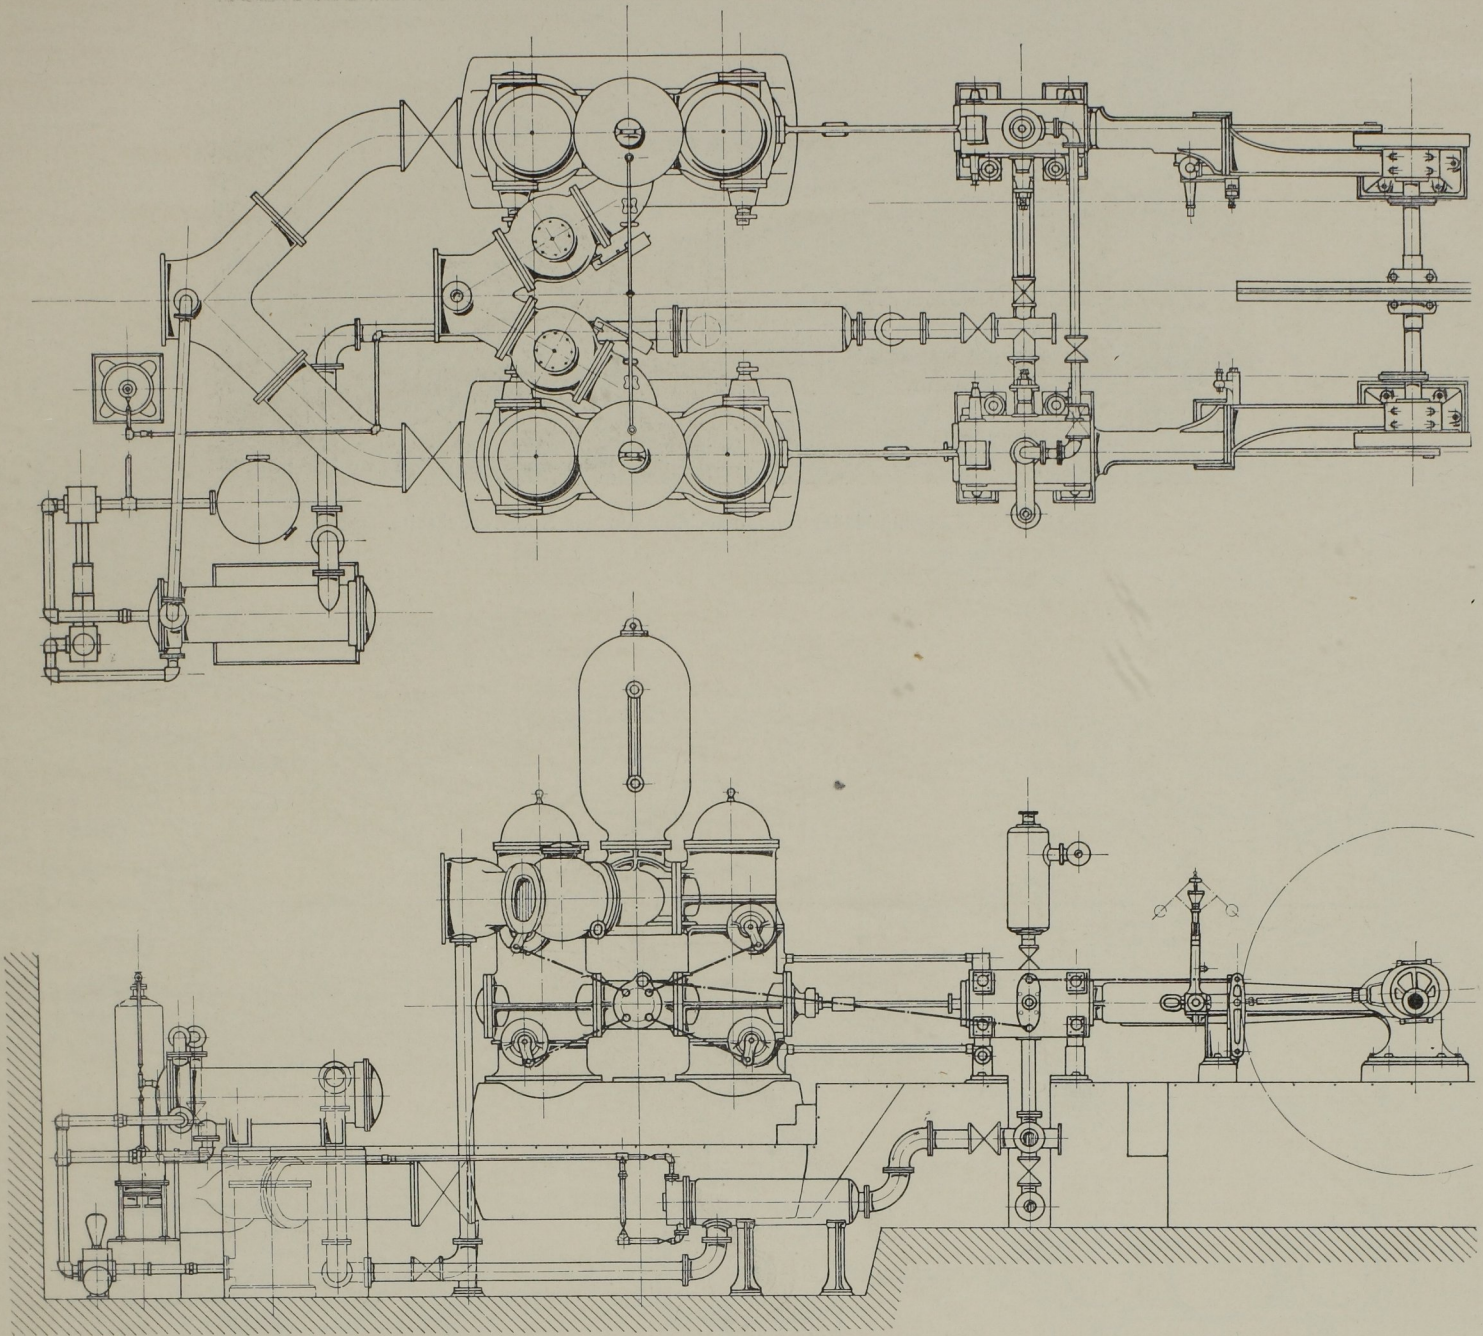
Grundriss und Seitenansicht. Massst. 1 : 72.
